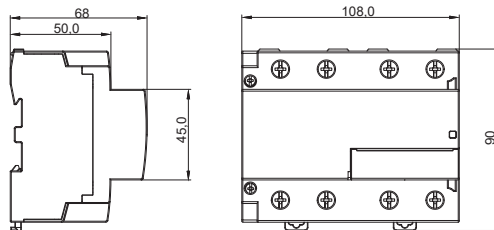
Габаритные размеры контакторов 100 А, 4P / Figure 6 – Overall dimensions of 100 A, 4P contactors
